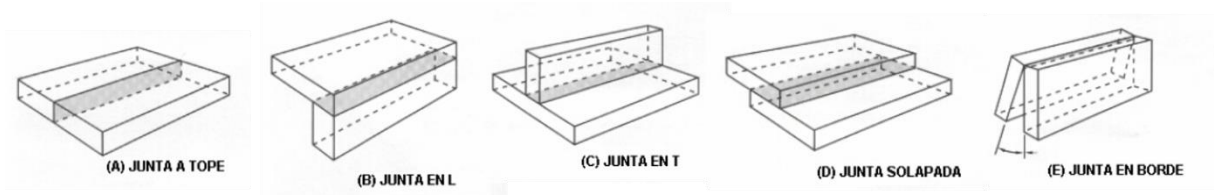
Configuraciones básicas de juntas para soldadura [68].
